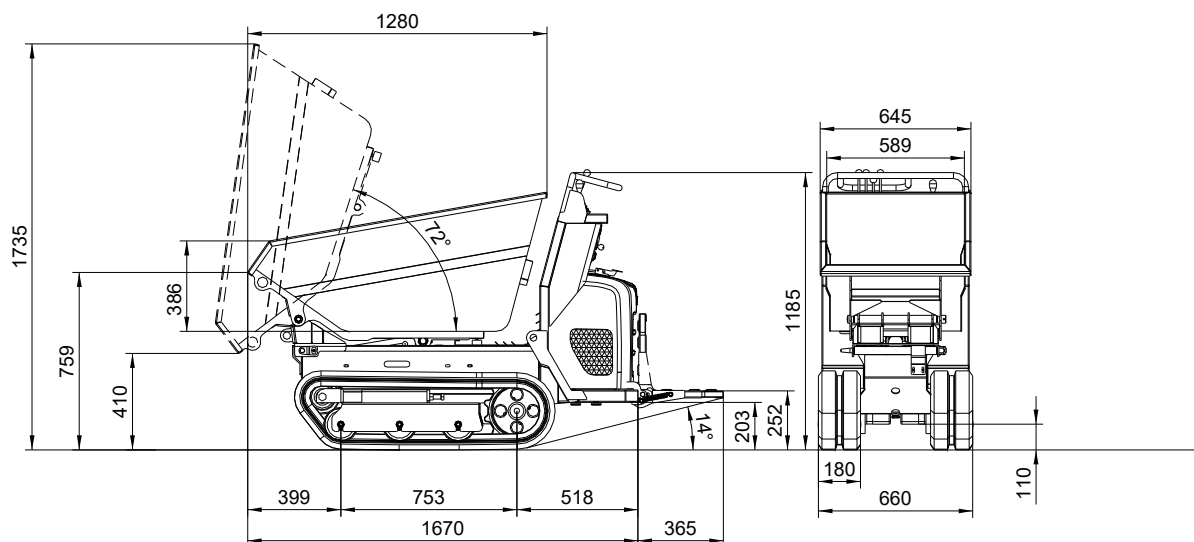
Dimensions de la machine (modèle DT05-D avec benne)
